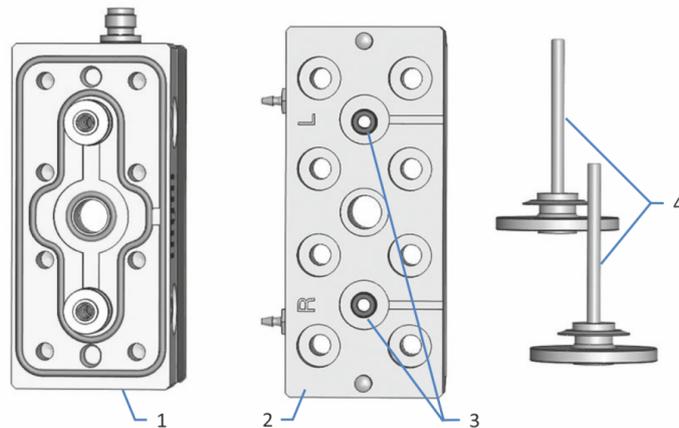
Tête de pompe, plaque de rinçage des joints et pistons retirés
